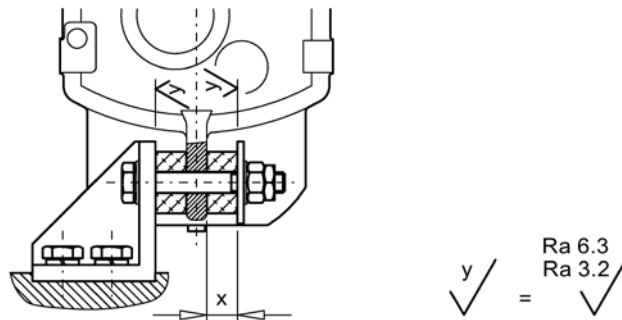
Montagevorschlag für Drehmomentstütze an F.28, 38B - 188B
